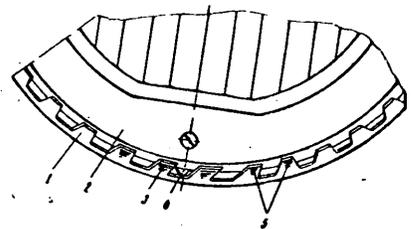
Расположение фиксатора-выступа ободка насадки в прямых зубцах отражателя: 1—отражатель; 2—насадка к фаре; 3—прямые зубцы отражателя; 4—фиксатор-выступ ободка насадки; 5—скошенные зубцы отражателя
